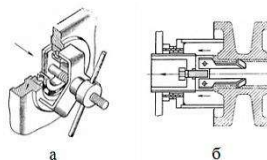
Специальные съемники для выпрессовки подшипников качения (а) и скольжения (б)
